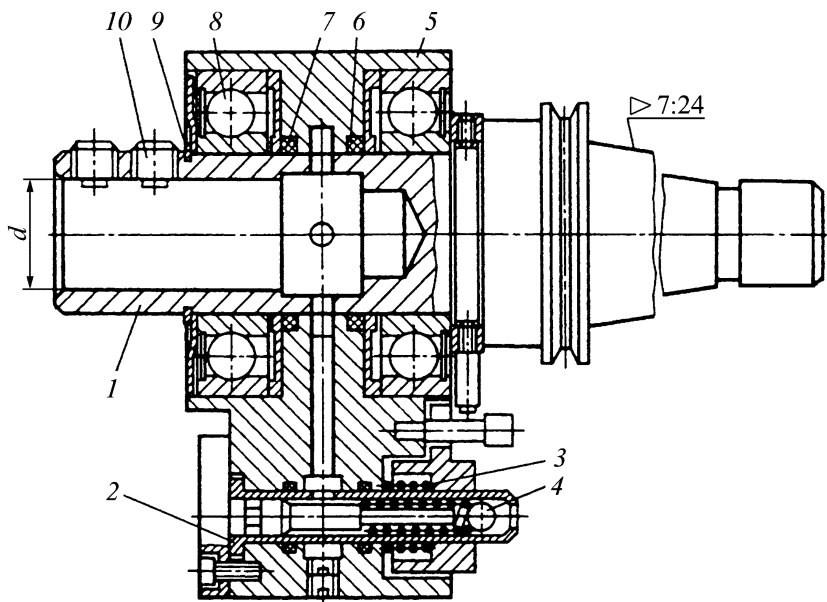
Патрон для подвода СОТС к вращающемуся инструменту
